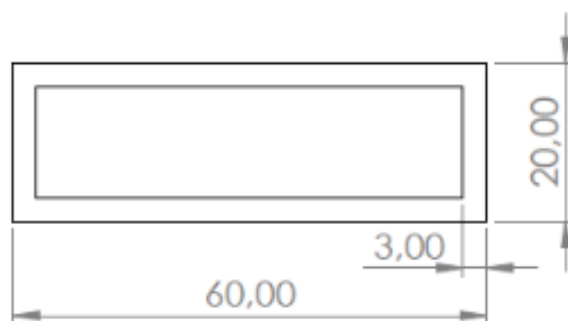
Perfil utilizado para as vigas de apoio verticais e para as vigas de suporte das chumaceiras
